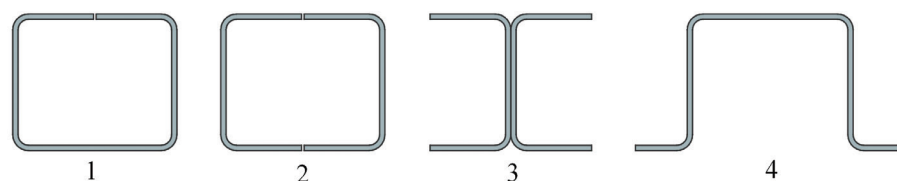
Виды сечений хребтовой балки из гнутого листового проката: 1 — прямоугольная труба; 2 — прямоугольная труба из двух С-образных профилей; 3 — двутавр из двух С-образных профилей; 4 — омегаобразный профиль
